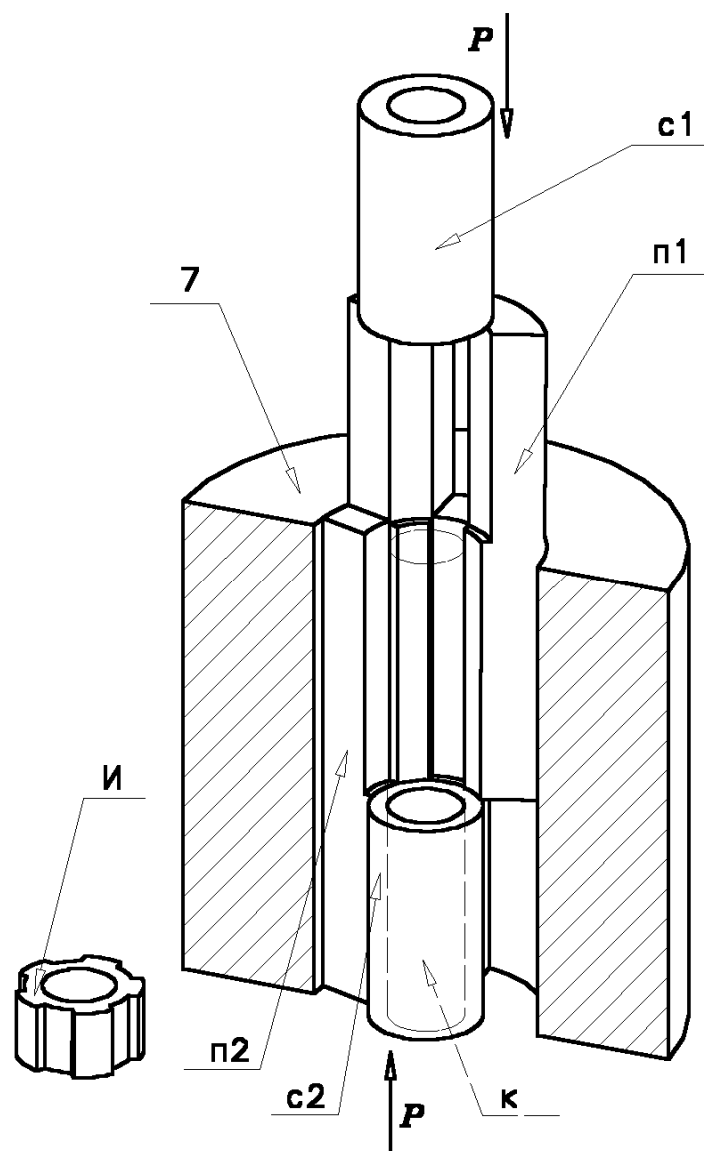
Пресс-форма для формования изделия в виде шестерни цилиндрической зубчатой передачи
